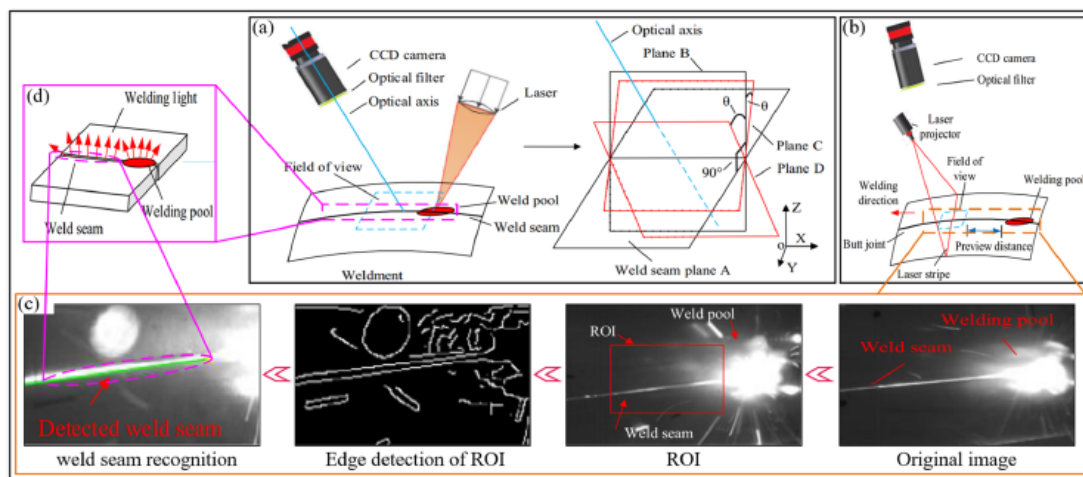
Ejemplo de control por visión en soldadura automática industrial. Fuente: [12]
